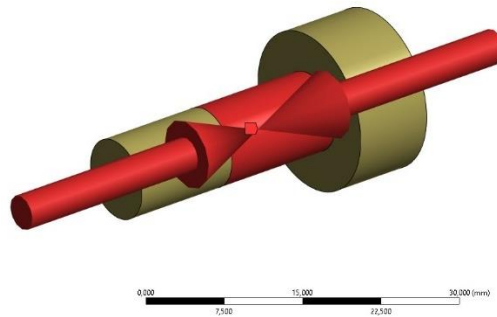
Použití kontaktu Frictional pro šroubový spoj
